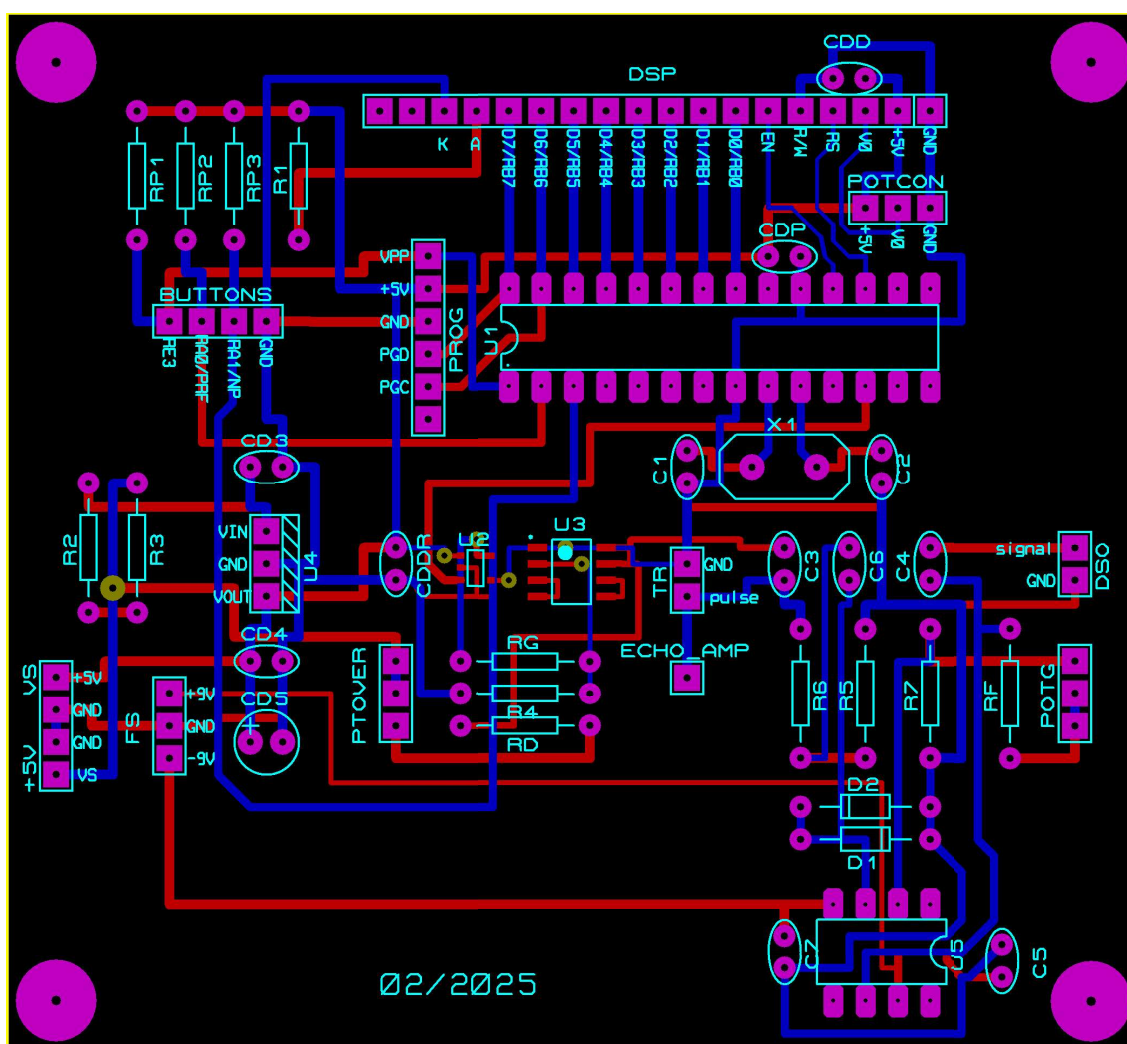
Layout* da parte inferior do cobre (*bottom copper*) da placa principal de circuito impresso dupla face.
